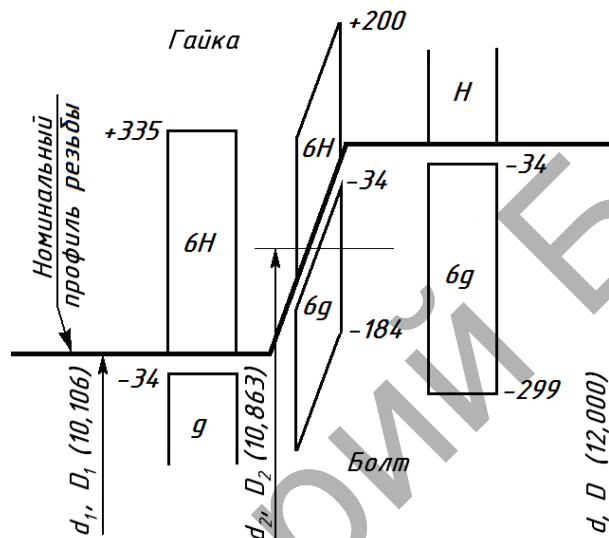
Схема расположения полей допусков резьбового соединения М12
